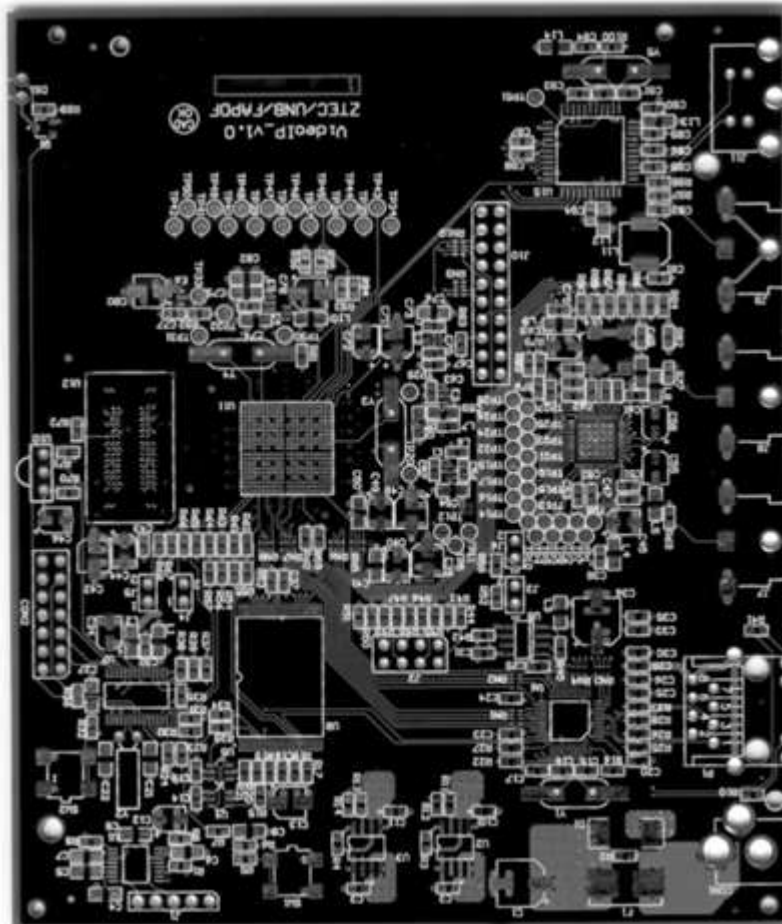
Placa de circuito impresso da plataforma Mídia-IP
